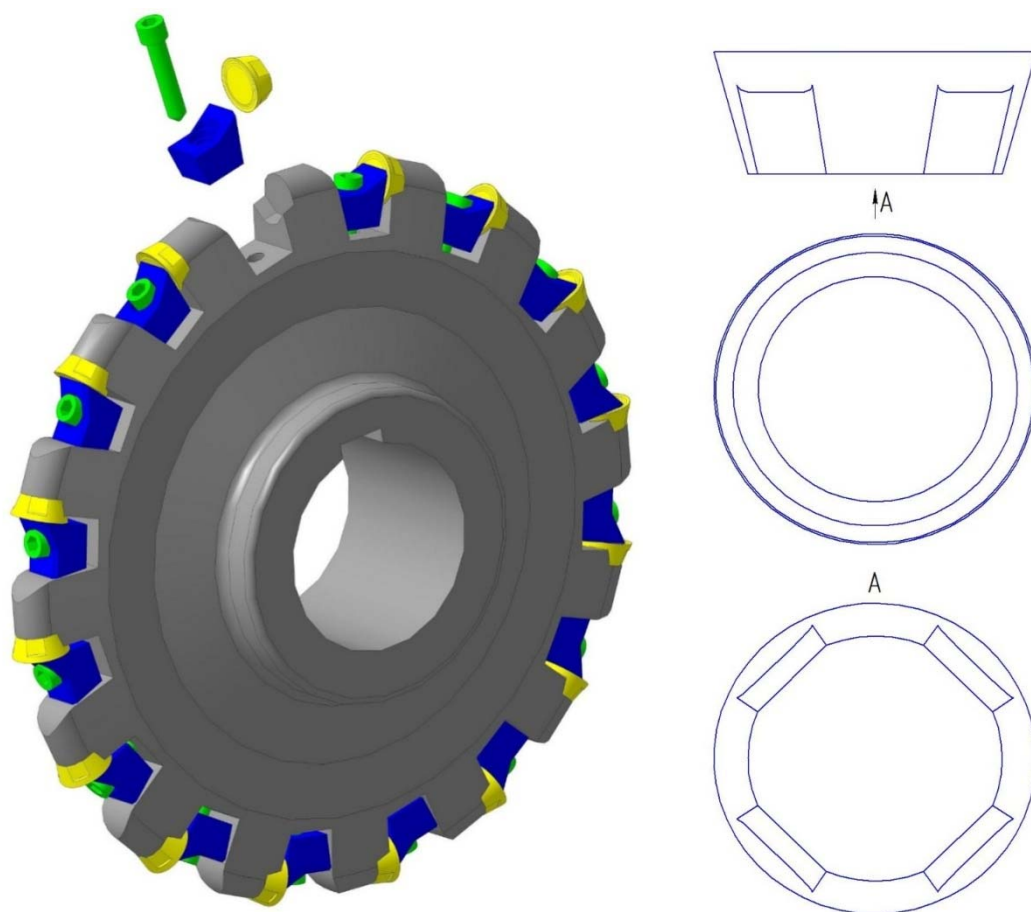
Разработанная конструкция сборной дисковой фрезы с круглыми усеченными под паз пластинами
